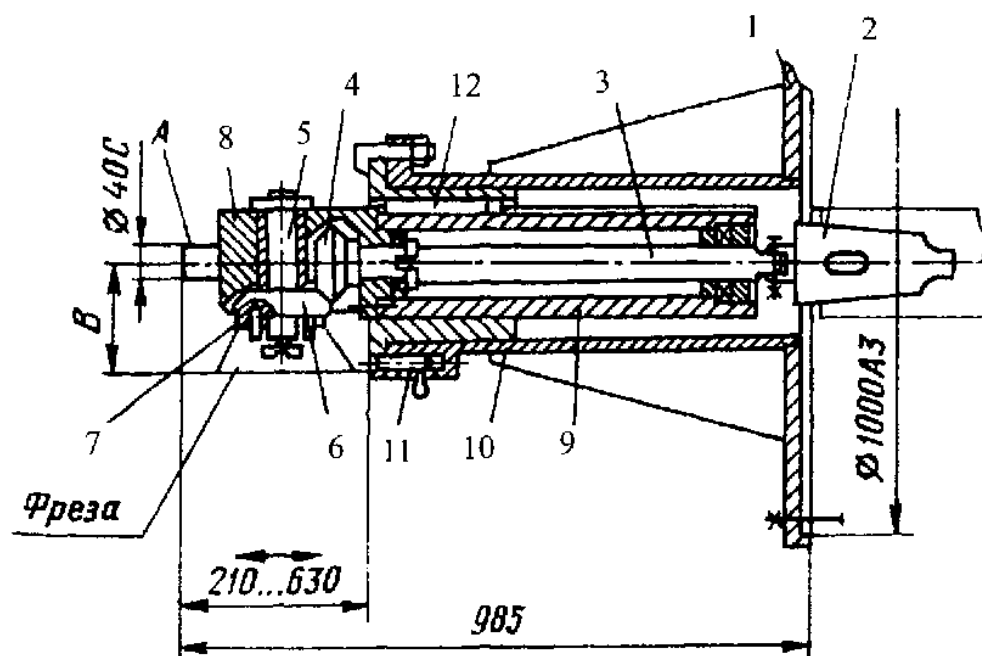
Фрезерна головка для обробки площин у важкодоступних місцях
